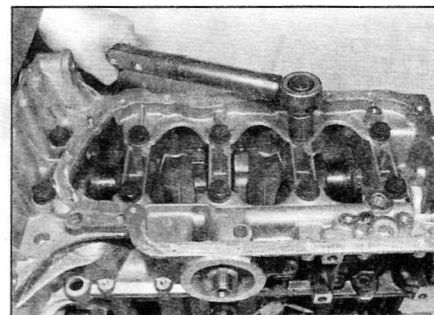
Затяните десять болтов коренных подшипников предписанным усилием (двигатели 1.4 л)
